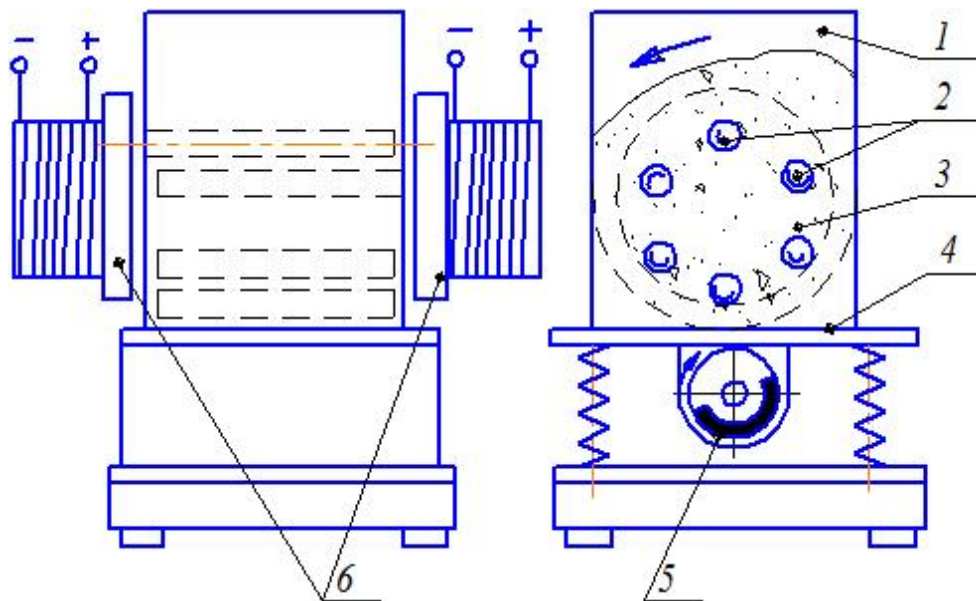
Схема пристрою для магнітновібраабразивної обробки
